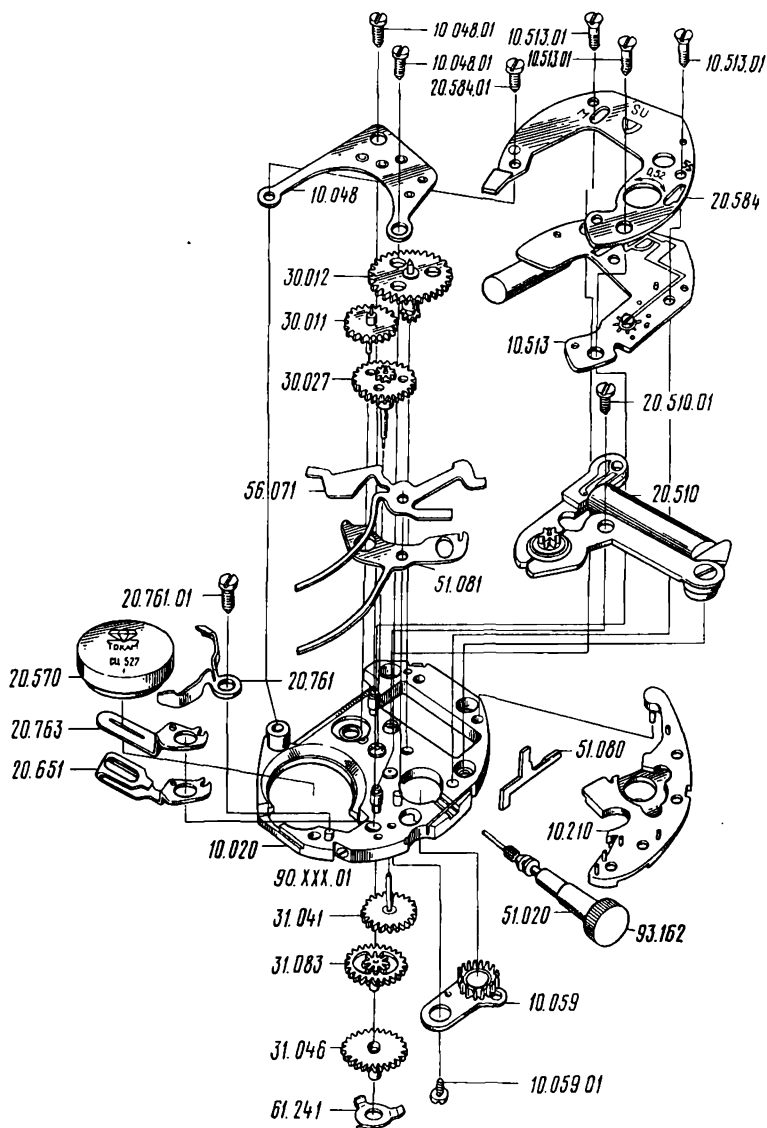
Детали и сборочные единицы механизма часов 1356:
